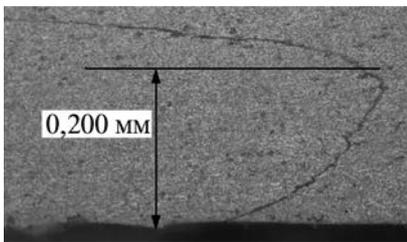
Непровар в корне сварного шва с малым раскрытием
